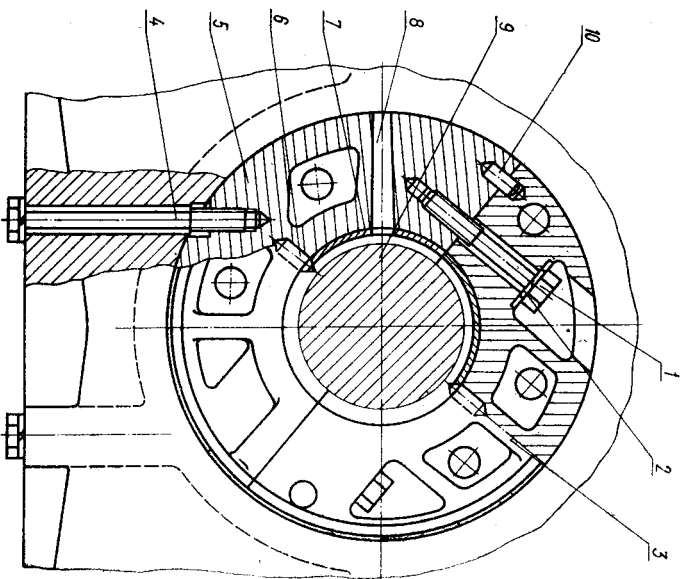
Опора среднего коренного подшипника (вид со стороны носка коленчатого вала):
